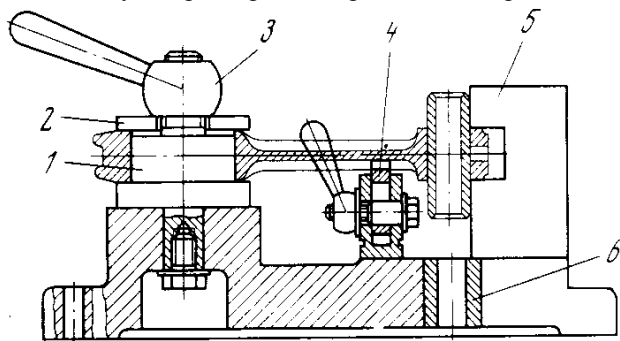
Приспособление для контроля и рихтовки шатунов: 1 — оправка; 2 — шайба; 3 — зажимная рукоятка; 4 — опора; 5 — шаблон; 6 — направляющая втулка.
